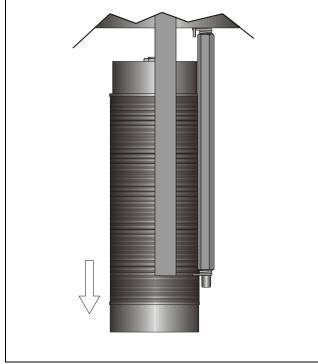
Démontage de l'ensemble de la bobine de filtre
